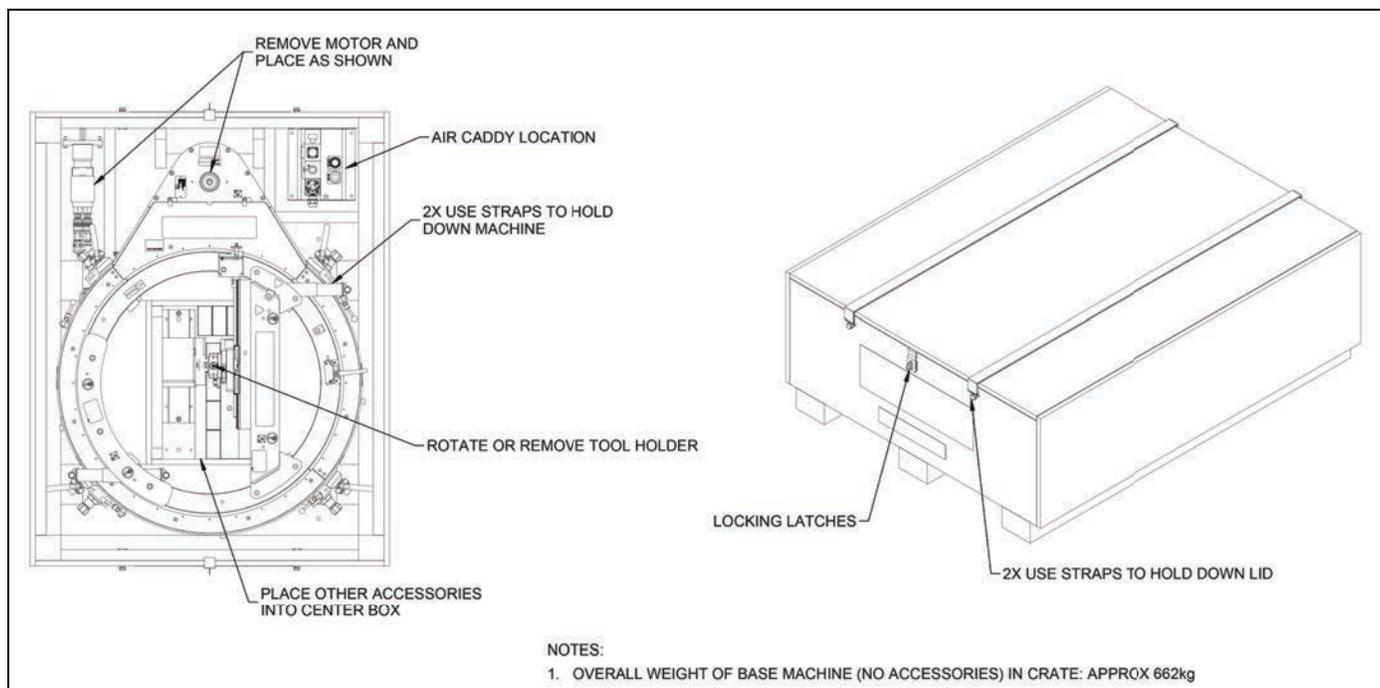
CAISSE D'EXPÉDITION DE LA MACHINE ODF30
